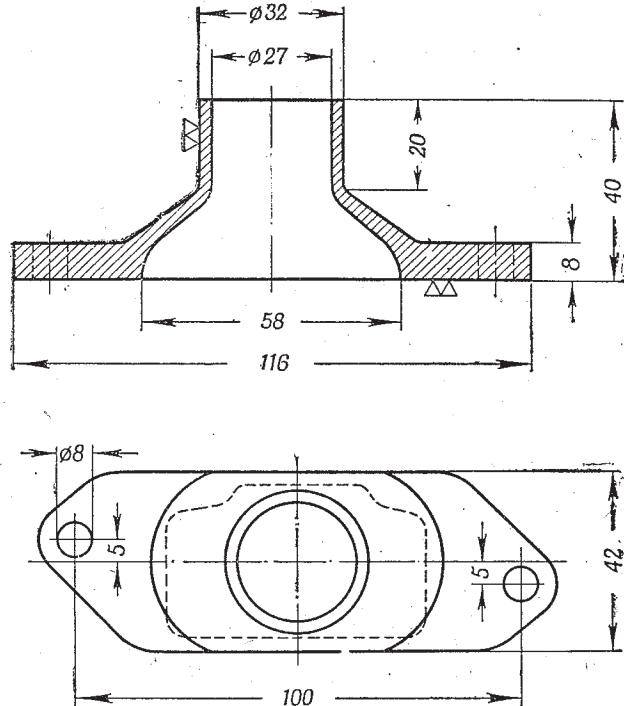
Впускной съемный патрубок для двигателя ИЖ-49
